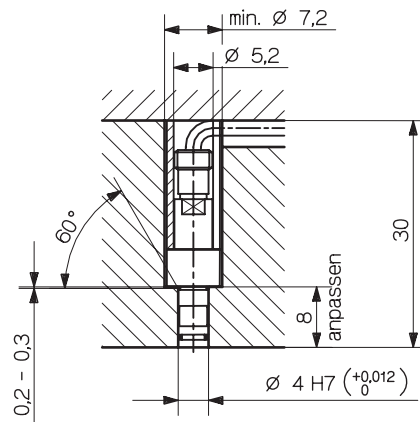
Einbau mit Distanzhülse (Typ 6459)
